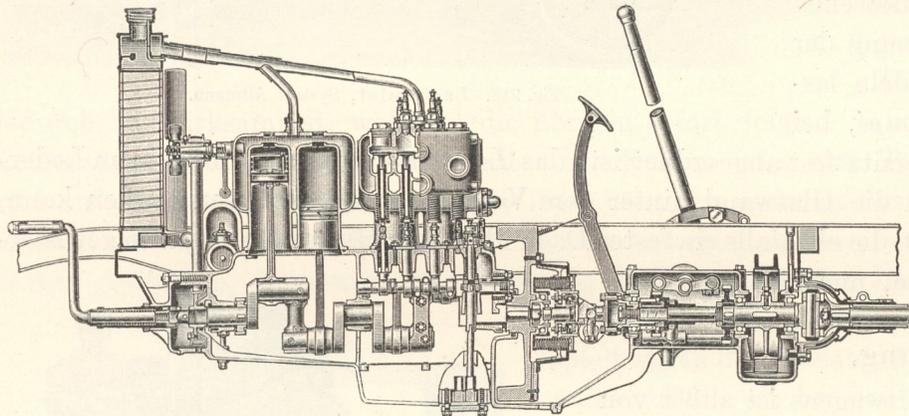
Schnitt durch den mit dem Getriebe zusammengebauten Motor eines Adler-Kleinautos.
